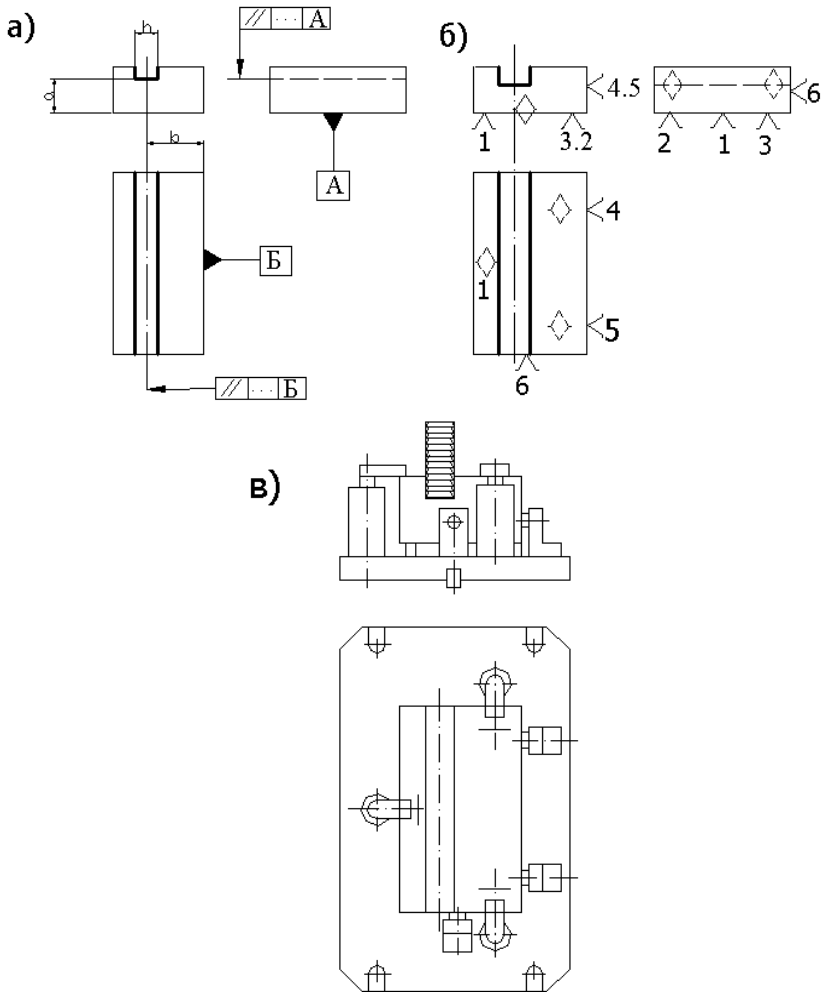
Разработка теоретической схемы базирования заготовки: а – заготовка; б – схема базирования; в – реализация теоретической схемы
